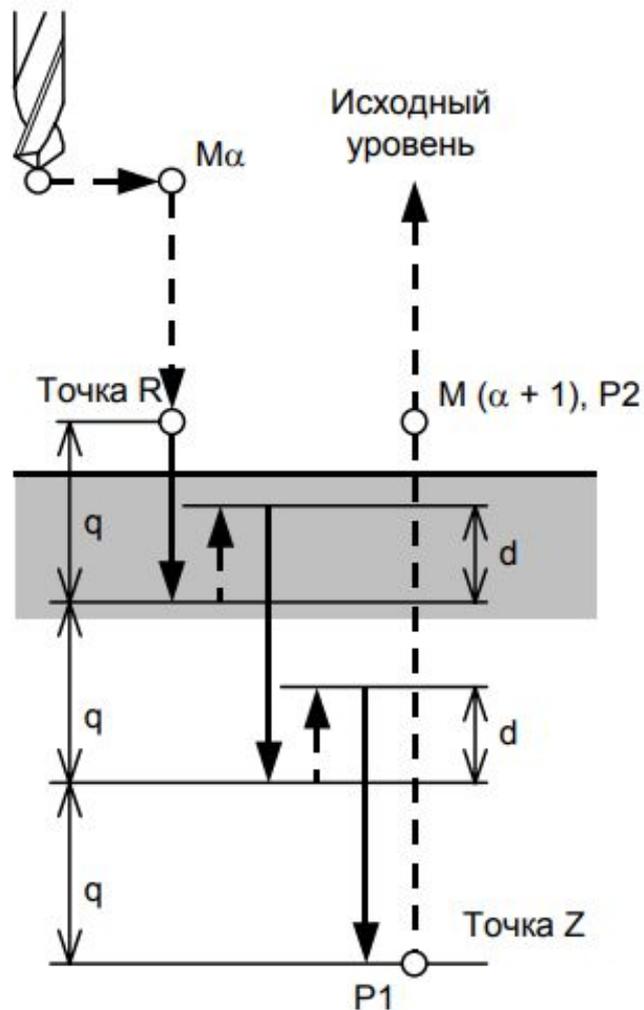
Цикл сверления передней и боковой поверхностей
